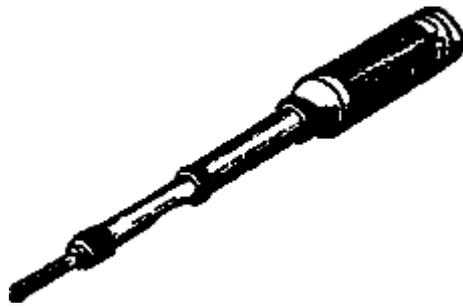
Автоматическая одноручная дрель для сверления отверстий под мелкие скобяные изделия
